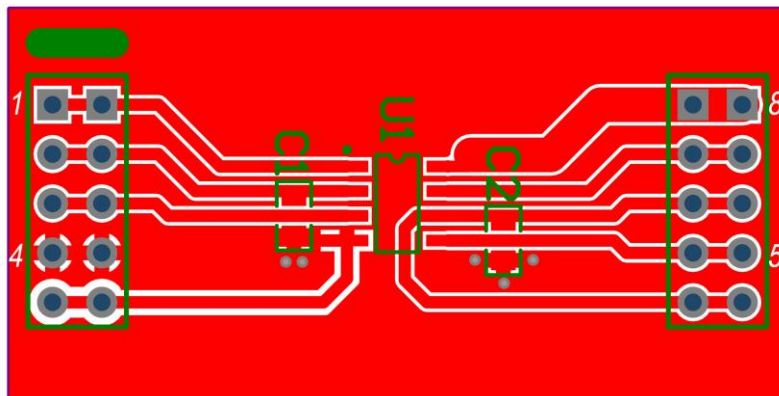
ZJR1003 评估板 PCB 布局 (顶层图)
